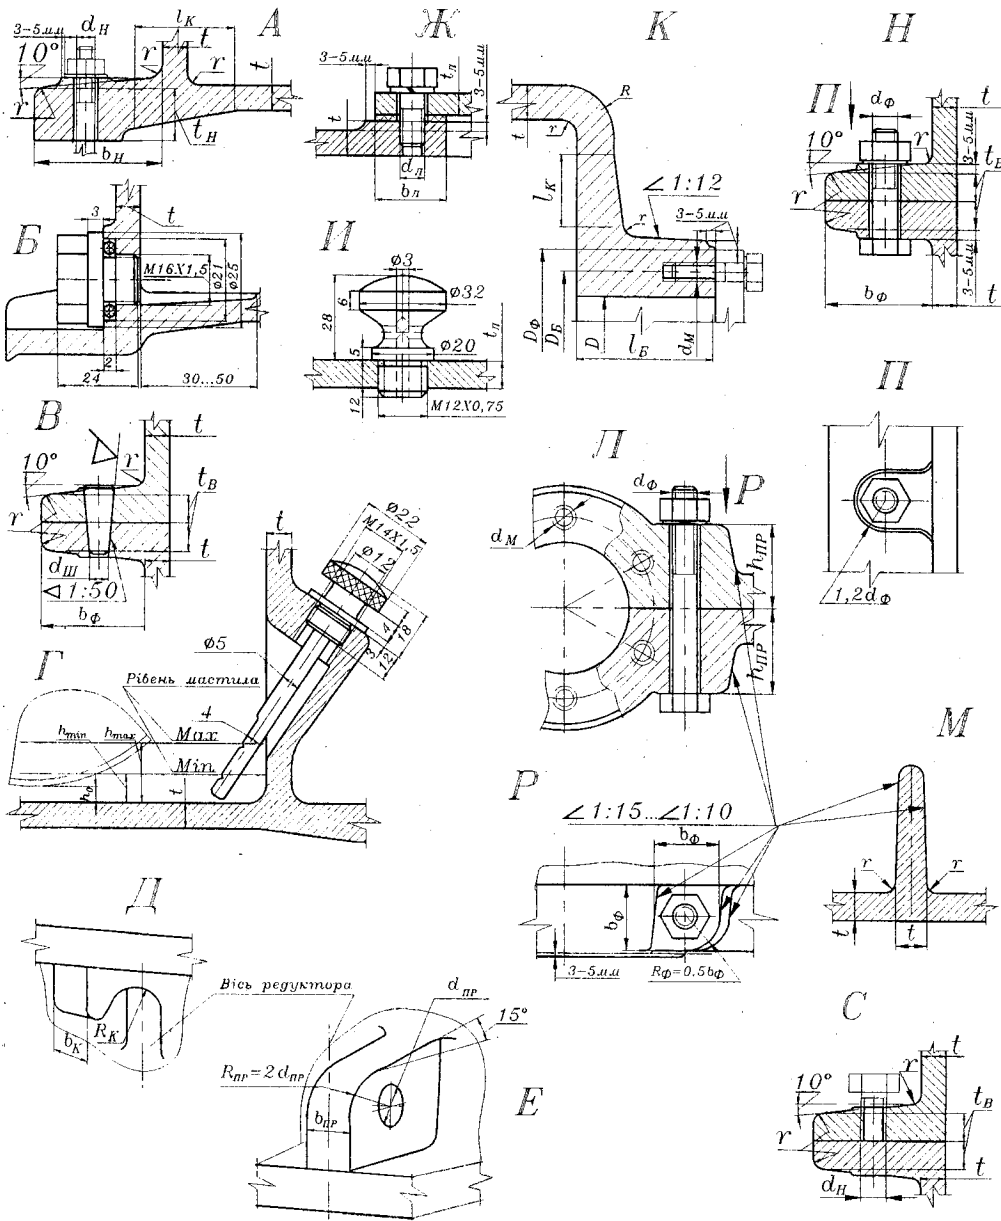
Схеми конструктивних елементів оболонки редуктора
